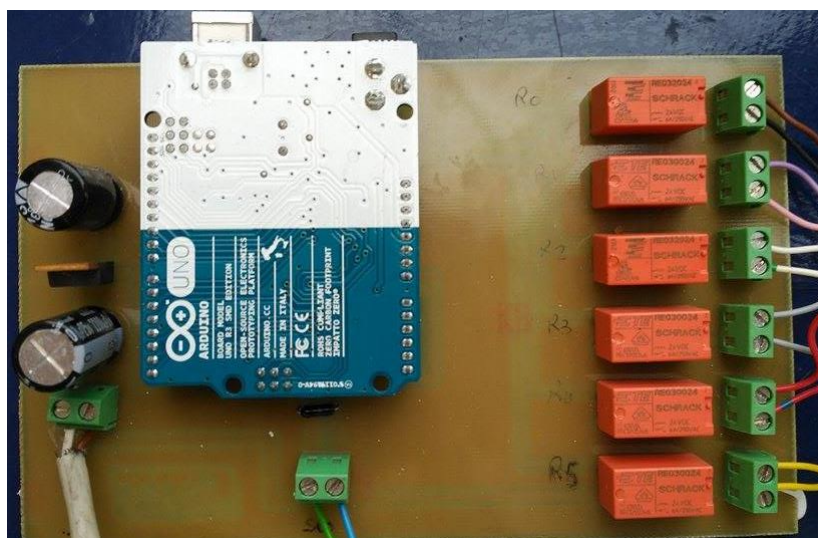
C Parte Superior del Circuito Integrado con Componentes Soldados y conexiones
